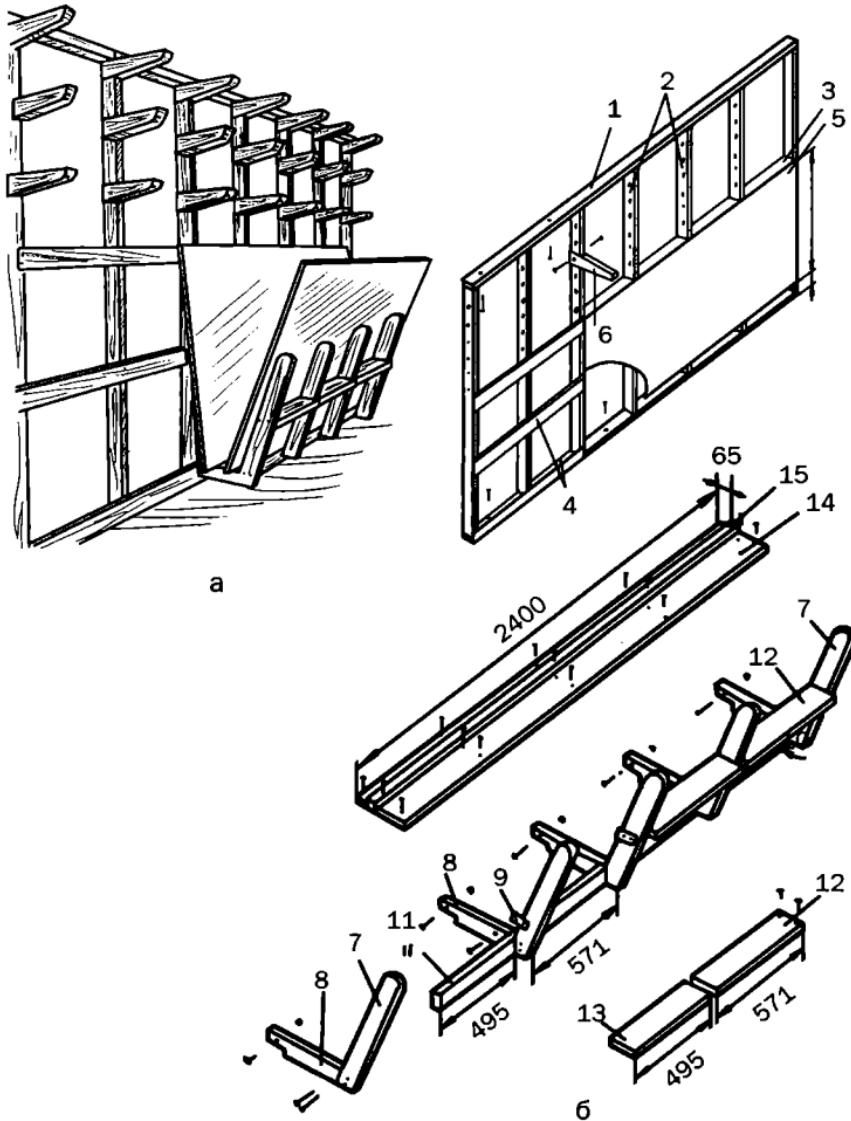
Стеллаж для хранения пиломатериалов (размеры указаны в миллиметрах): а — общий вид; б — схема сборки; 1 — верхняя (нижняя) обвязка; 2 — стойки; 3, 10, 11 — приставки; 4 — стяжки; 5 — задняя стенка; 6 — боковые доски; 7 — наклонные опоры; 8 — напольные опоры; 9 — планка; 12, 13 — ступеньки; 14 — пол; 15 — бруск.
